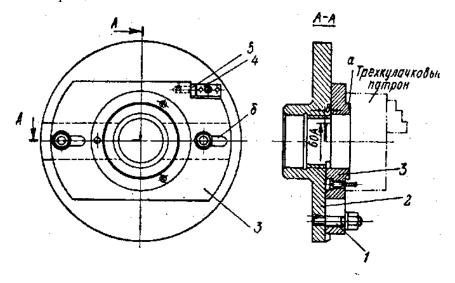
Приспособление с передвижным кулачковым патроном для обработки деталей (поверхностей) с параллельными осями
